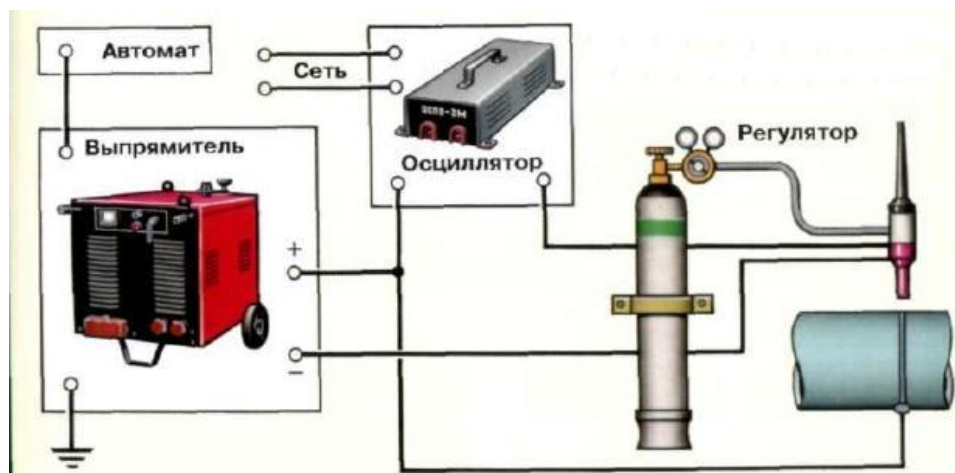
Схема выполнения сварки неплавящимся электродом в защитных газах
